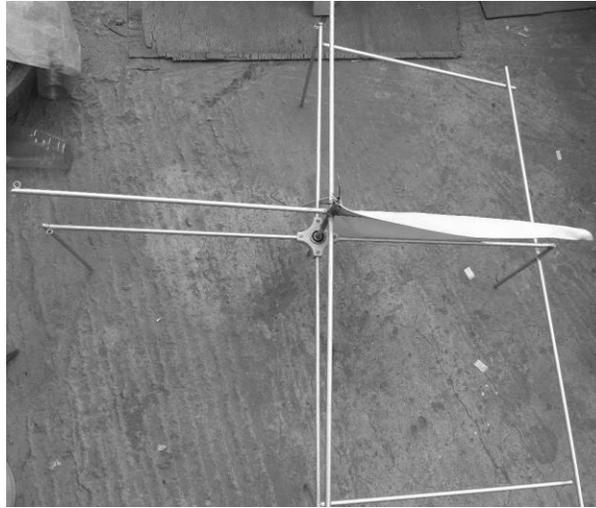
Soldadura antigénica con aporte de silicio para la unión de los tubos de aluminio anodizado.
